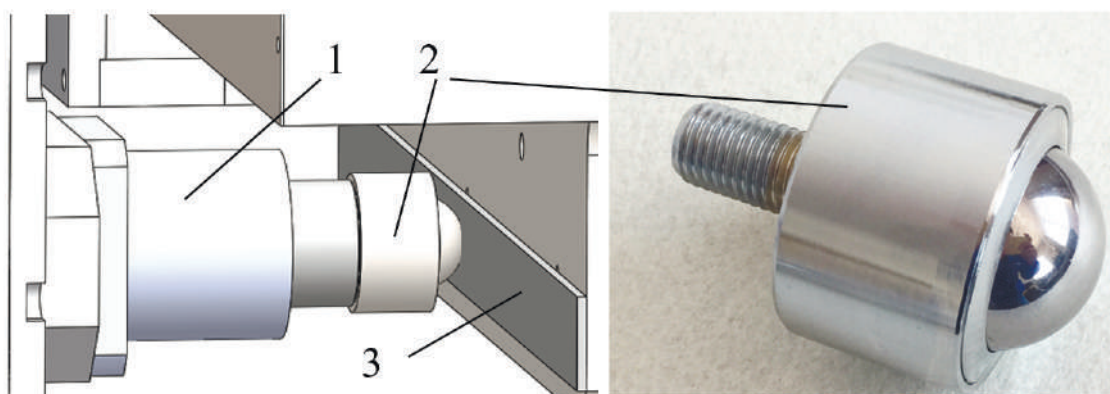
Уравновешивающий механизм: 1 – линейный подшипник,
